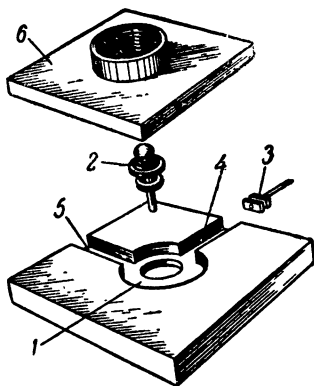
Основные детали камерного детектора миллиметровых волн.
